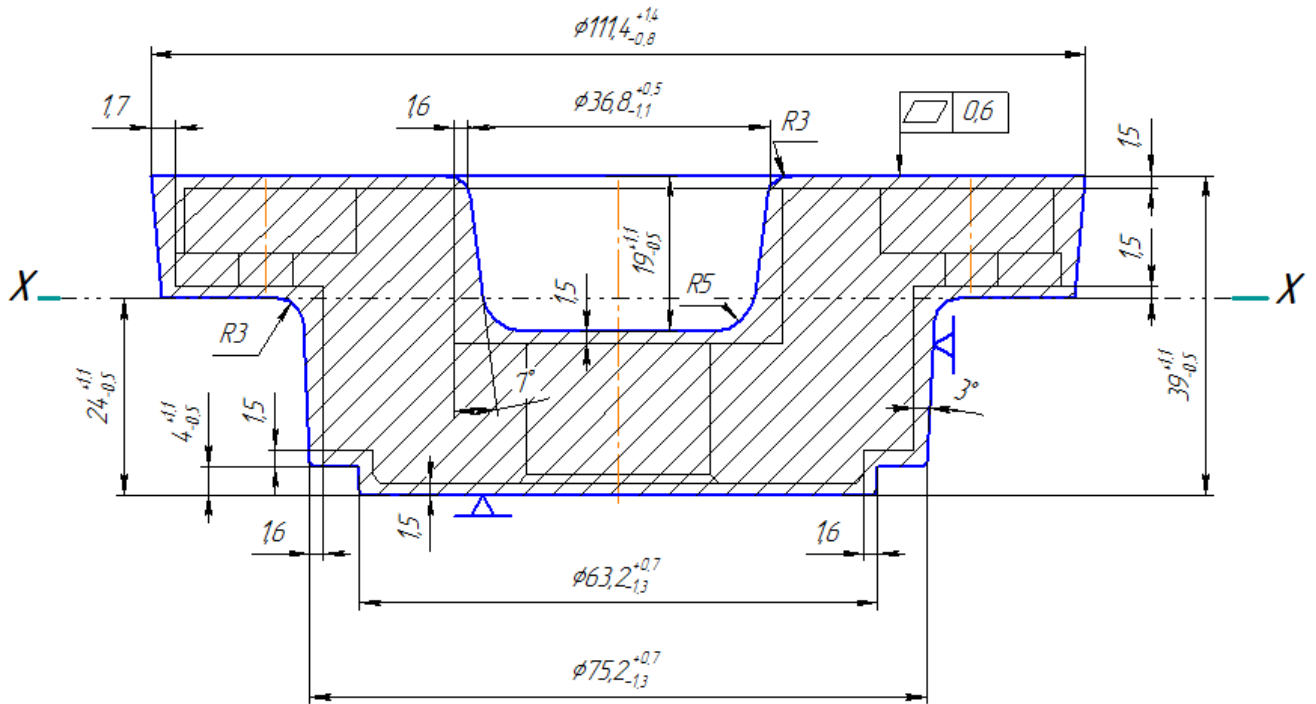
Ескіз заготовки отриманої методом штампування
